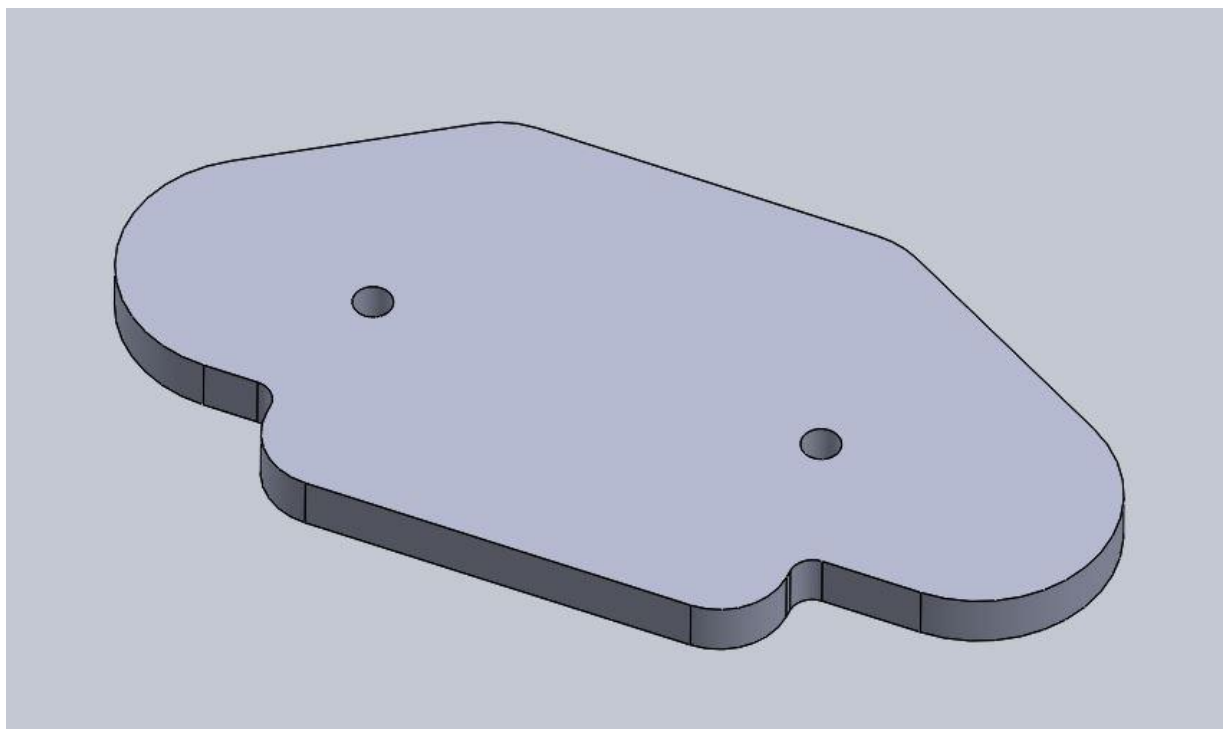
3D модель заготовки деталі «Куліса двигуна катерки Y»
